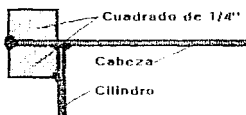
Corte de soldadura entre cilindro y cabeza.
